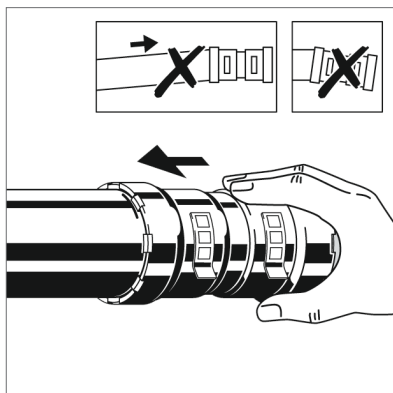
Pressverbinder – ohne zu verkanten – bis zum Anschlag auf das Rohr schieben.
